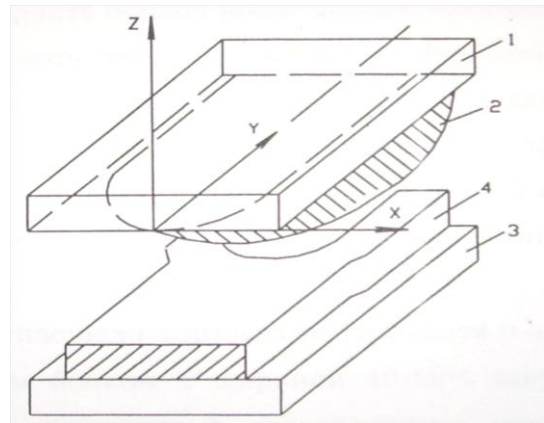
Ковка полосы эллипсоидным бойком [14]: 1 и 3 – верхняя и нижняя плоские плиты; 2 – эллипсоидный боек; 4 – заготовка
